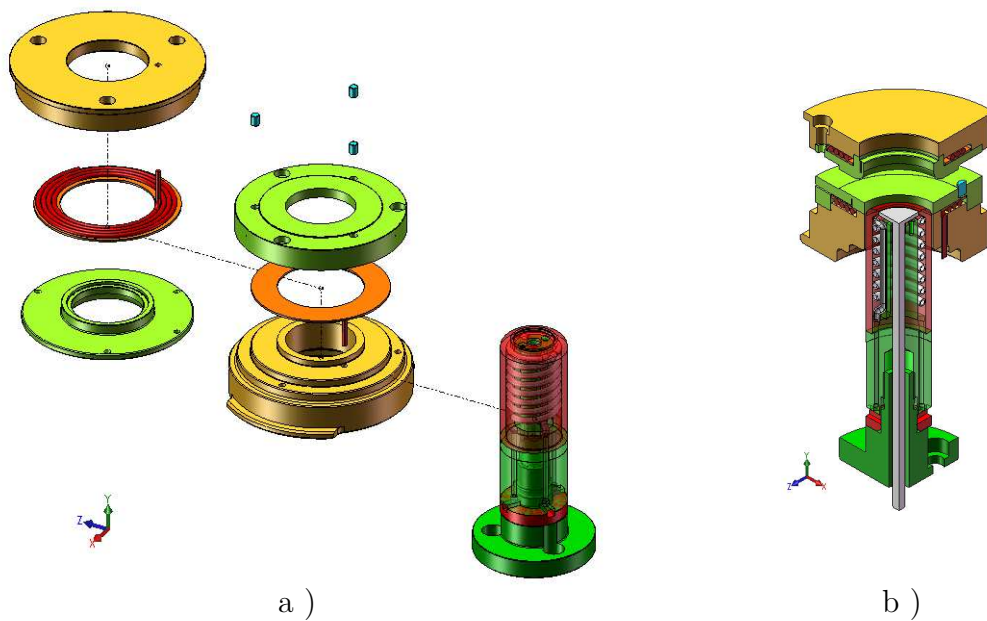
Représentation CAO du dispositif conçu. a) Vue éclatée et b) Vue quart coupée.
